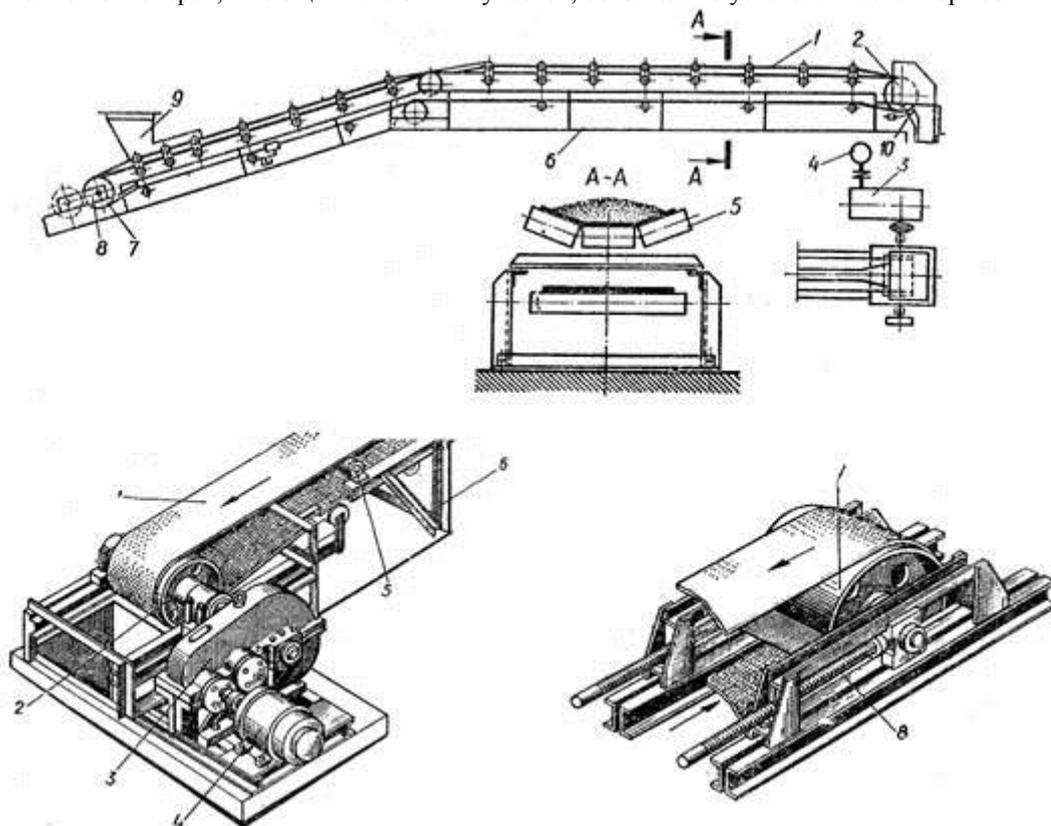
Общий вид ленточного конвейера: а – компоновочная схема; б – приводная станция; в – натяжная станция; 1 – лента;
